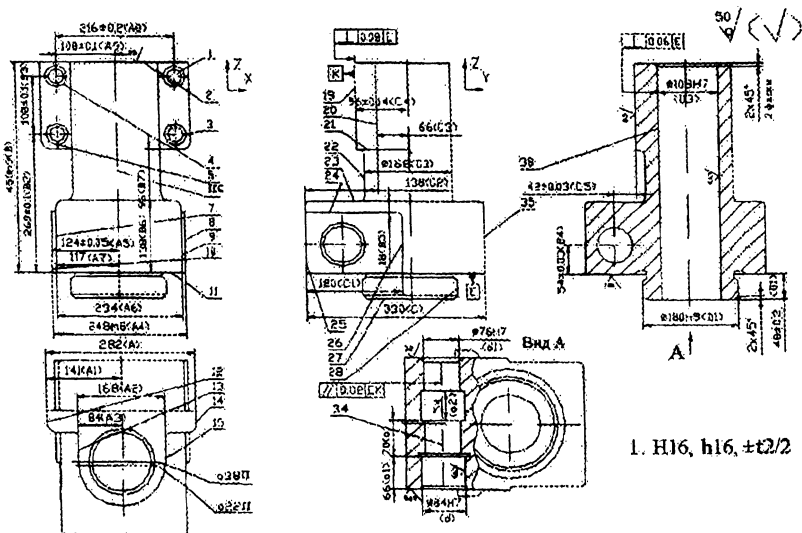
Эскиз детали с нумерацией поверхностей и обозначением кодов размеров
